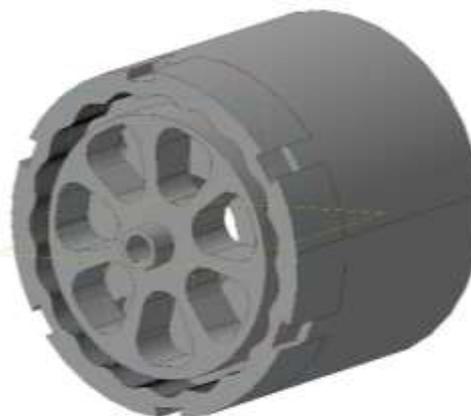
3D-сборка волновой передачи со снятой крышкой (без тел качения)
